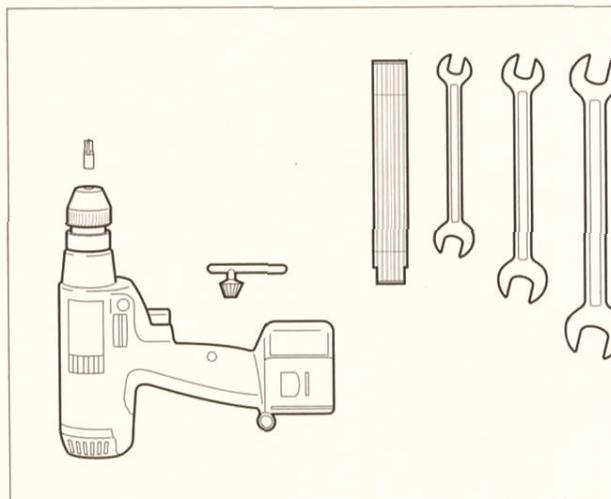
Montage-Werkzeug: Zollstock, Bohrmaschine, Kreuzschlitz-Bit PZ3, Maulschlüssel in den Größen 16, 19 und 24
